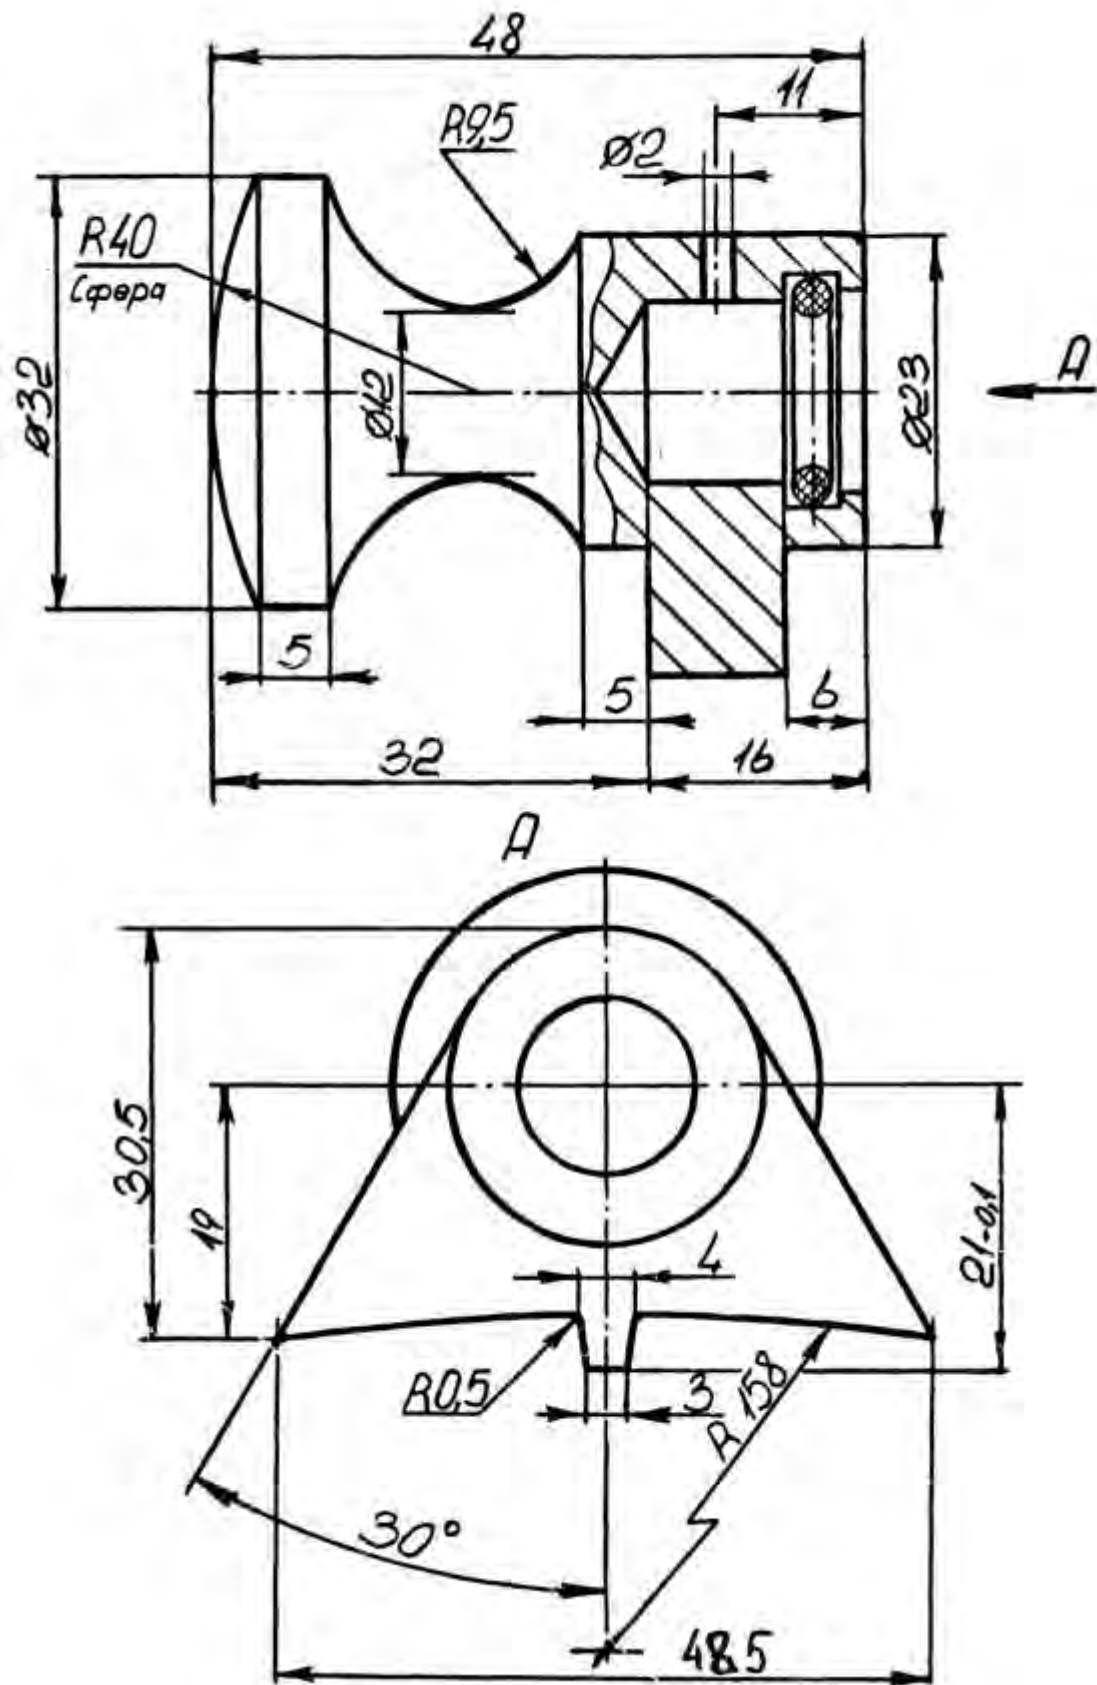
3М 7820-4550 Фиксатор коленчатого вала
